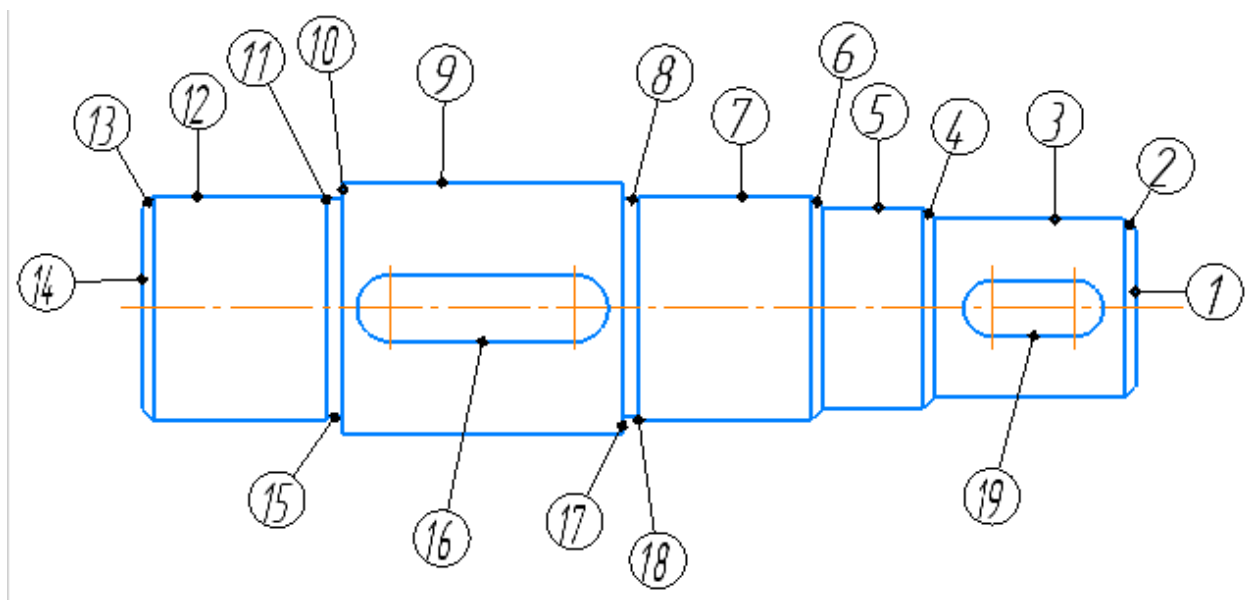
Схема детали «Вал» с обозначением нумерации
